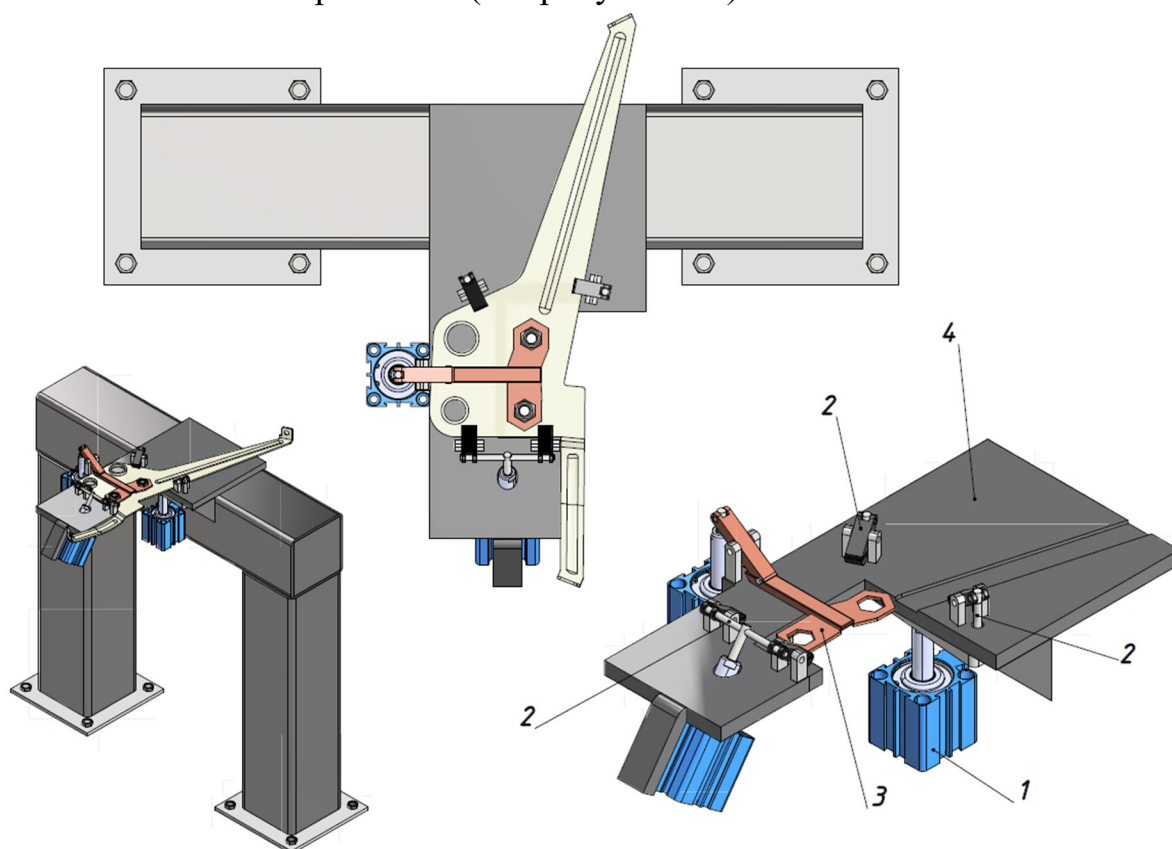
Стойка с системой прижимов для фиксации заготовок для сваривания. 1-пневмоцилиндр SDA 32-10, 2-система прижимов, 3-фиксатор для гаек, 4-установочная платформа для заготовок.
